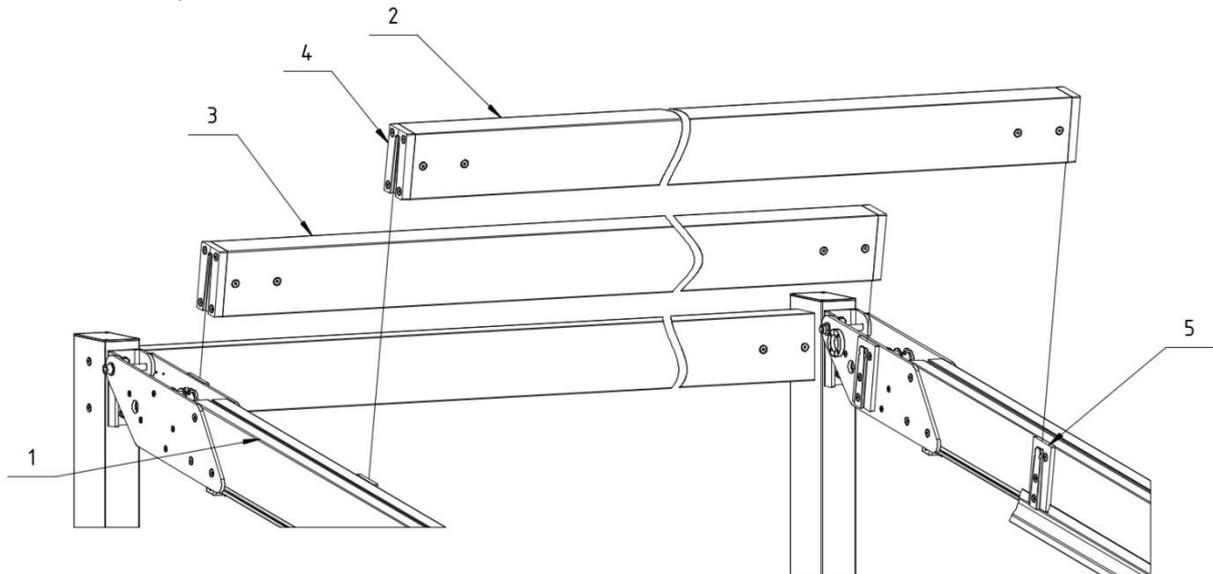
Montage des poutres de raidissement: 1 – Poutre de guidage , 2 – Poutre de raidissement (avant), 3 – Poutre de raidissement (arrière) , 4 – Pochette Sherpa, 5 - Sherpa.
